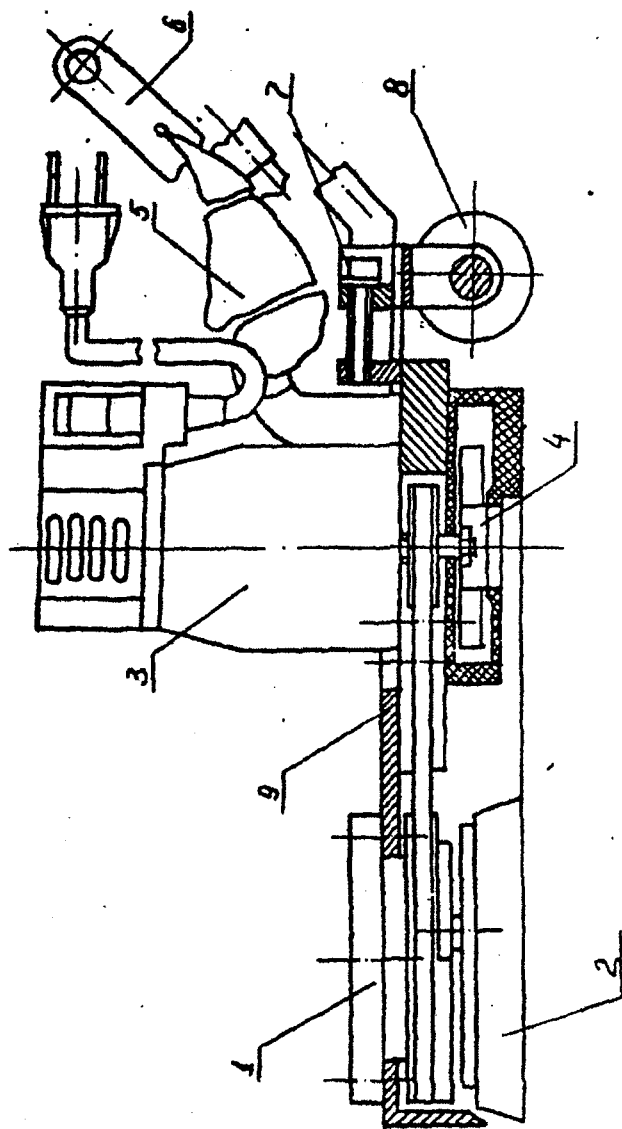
Машина для механической обработки полов с планетарным движением инструмента: 1 – планетарный механизм; 2 – рабочий инструмент; 3 – коллекторный электродвигатель с выключателем и токоподводящим кабелем; 4 – вентиляционное устройство; 5 – пылесборник; 6 – рукоятка управления; 7 – клиноременная передача; 8 – ходовое устройство; 9 – рама машины
